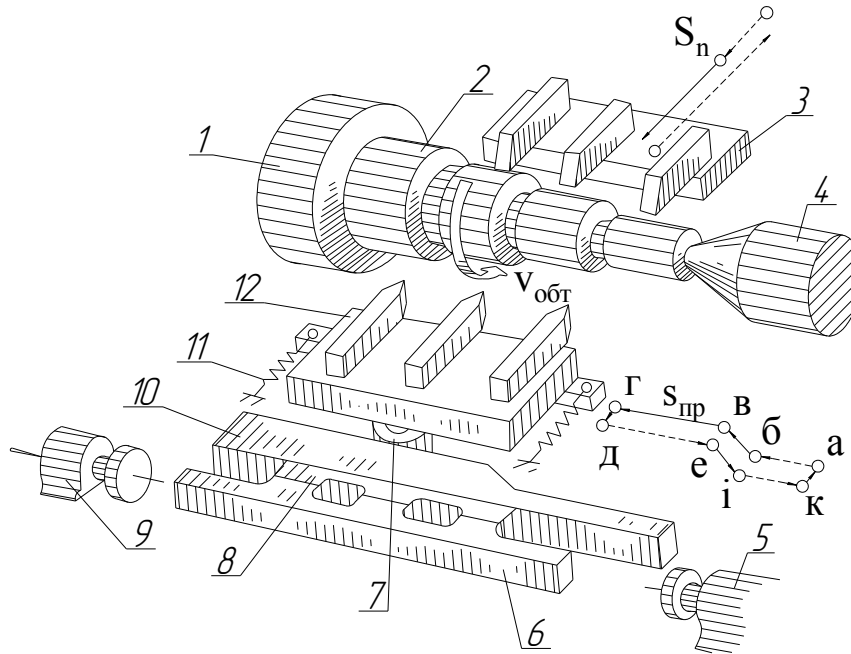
Схема роботи багаторізевого напівавтомата.
